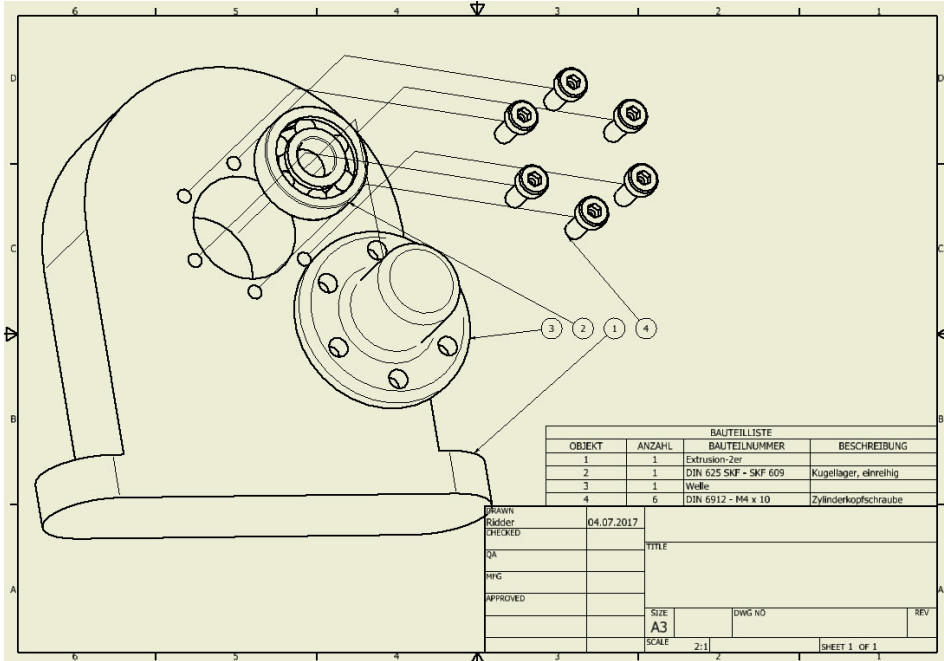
Zeichnung der Explosionsansicht mit Positionsnummern und Stückliste
